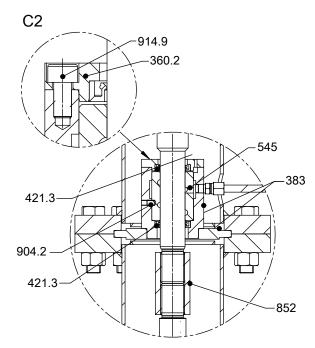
Detailzeichnungen Gewindekupplung (nur bei Ausführung mit 2 oder 3 Zwischenrohren)
